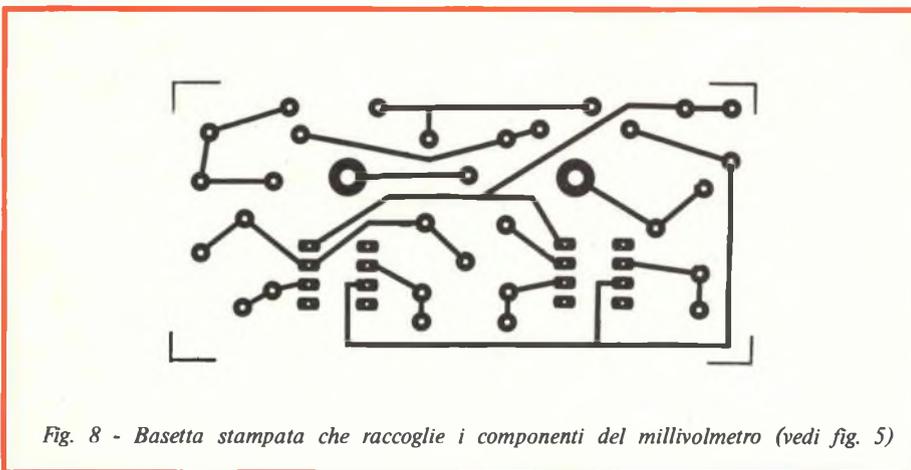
Basetta stampata che raccoglie i componenti del millivolmetro (vedi fig. 5)
